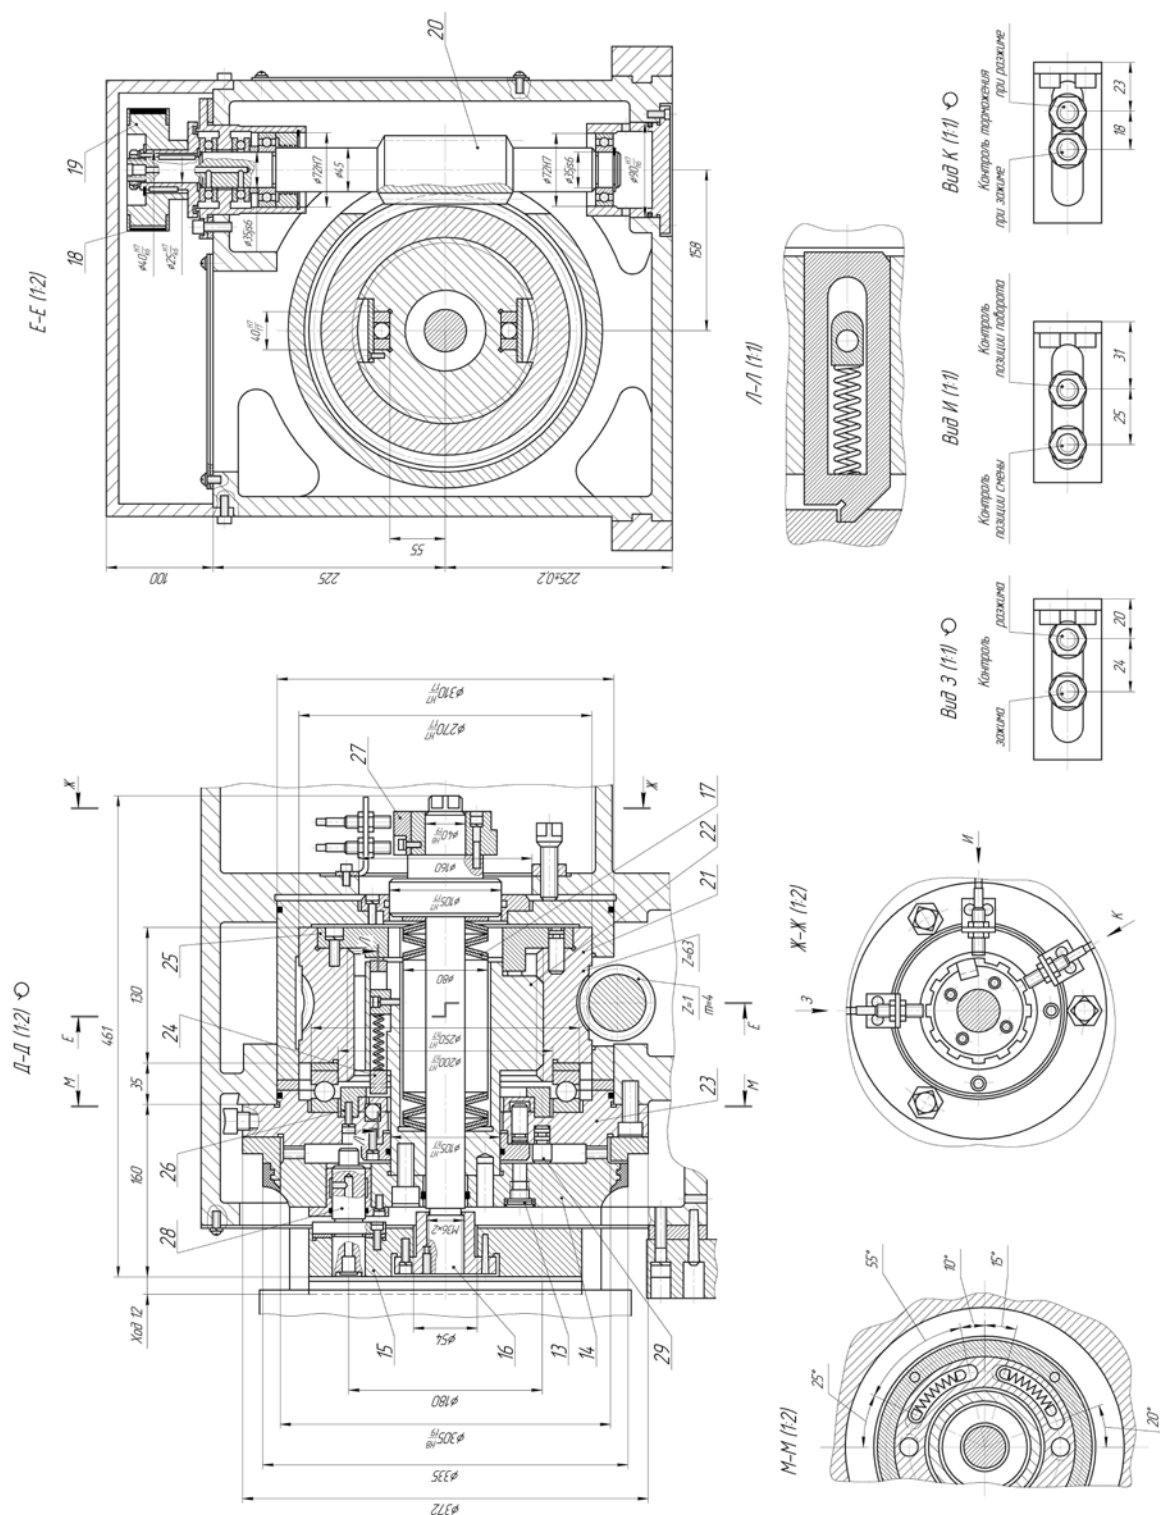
б. Разрезы механизма поперечно-подвижного суппорта и револьверной головки станка ИРТ180ПМФ4
